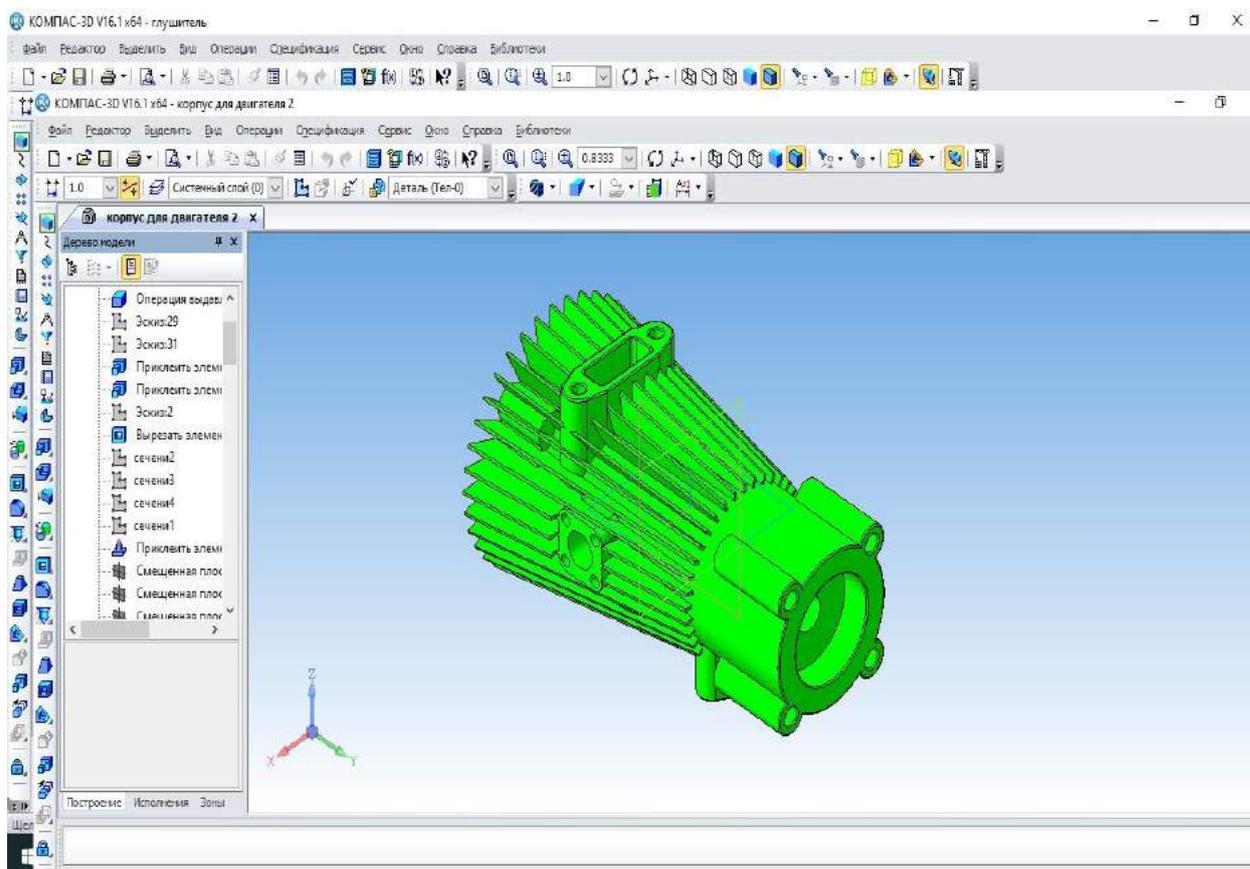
Скриншот детали «Крышка для двигателя 2» в3D – детализовке
